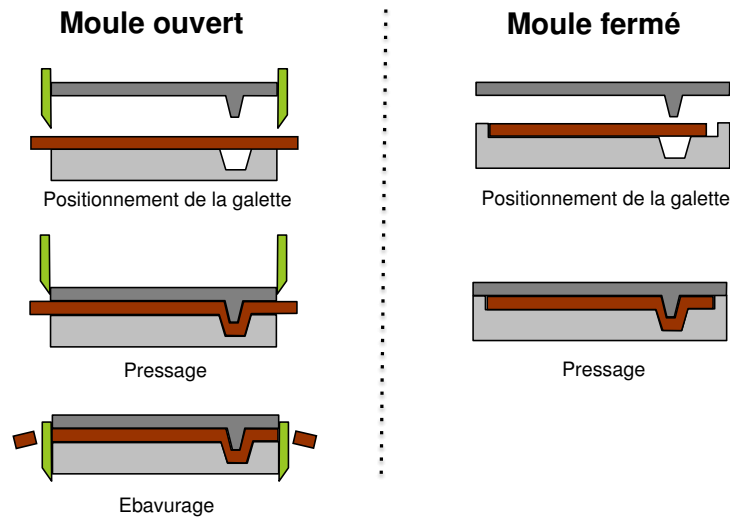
Schéma de principe de l'estampage en moule ouvert et en moule fermé
